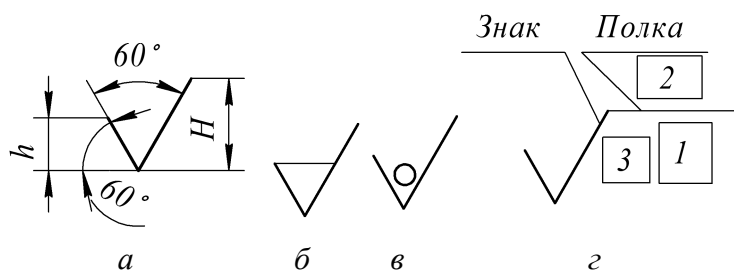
Знаки, используемые для обозначения шероховатости на чертежах
